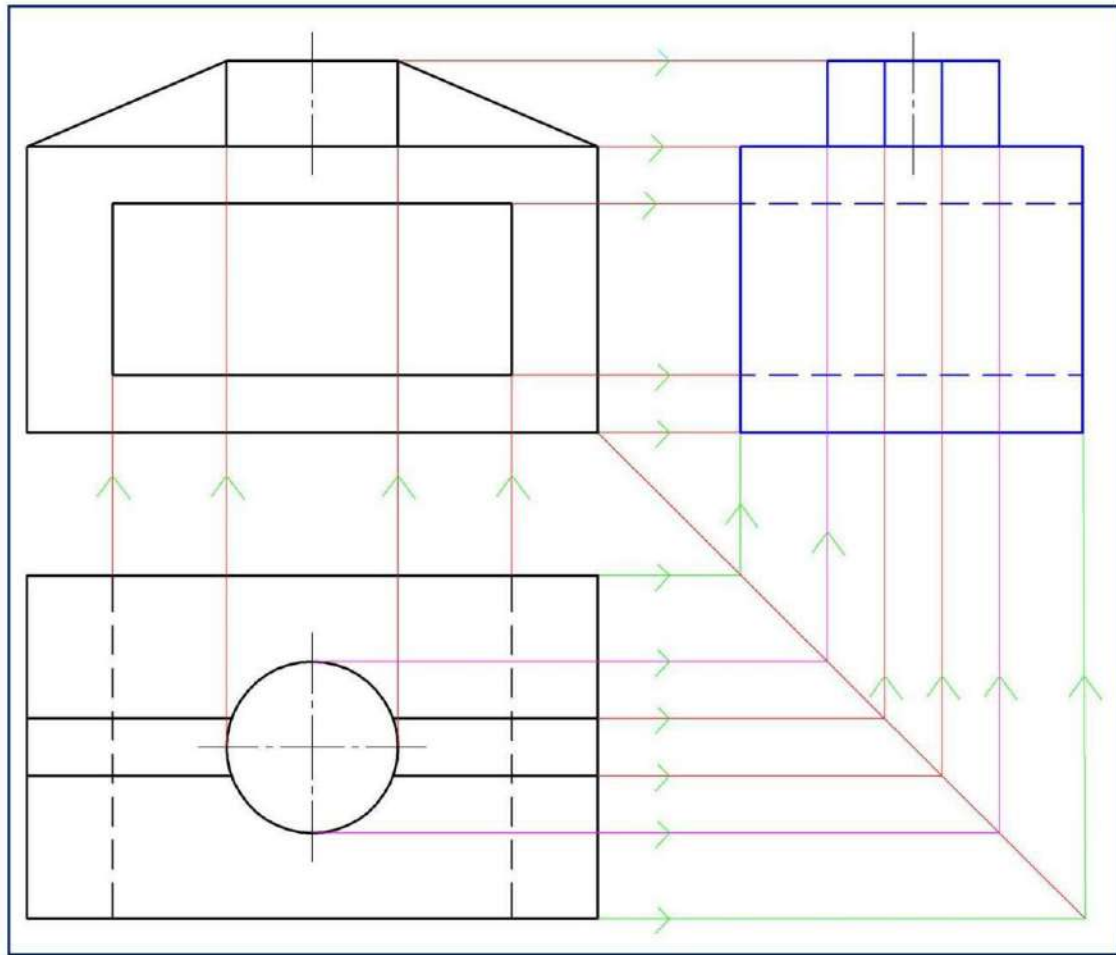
أ المسقط الأمامي والمسقط الأفقي لجسم
